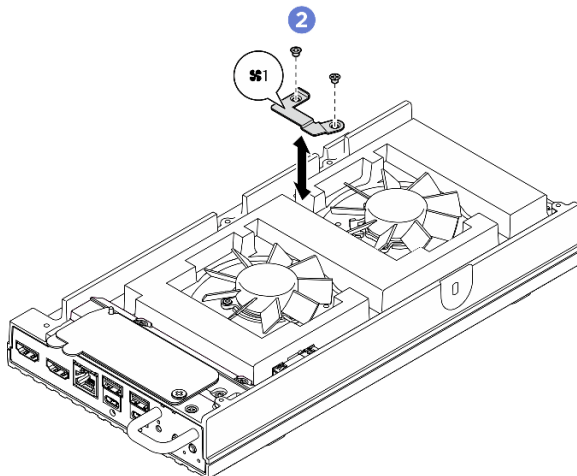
Schraubenposition der Halterung für Lüfter 1
